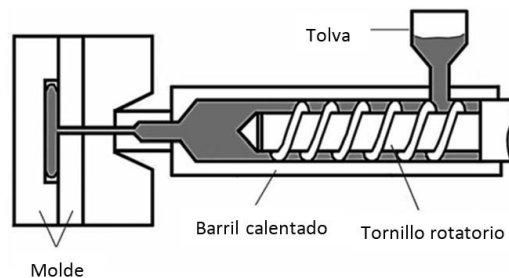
Máquina de moldeo por inyección de tornillo recíprocante [3].
